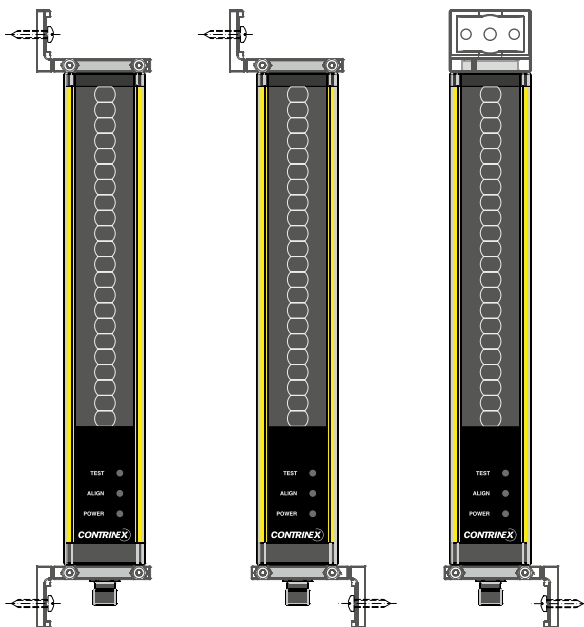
DIFERENTES POSSIBILIDADES DE MONTAGEM COM SUPORTES
